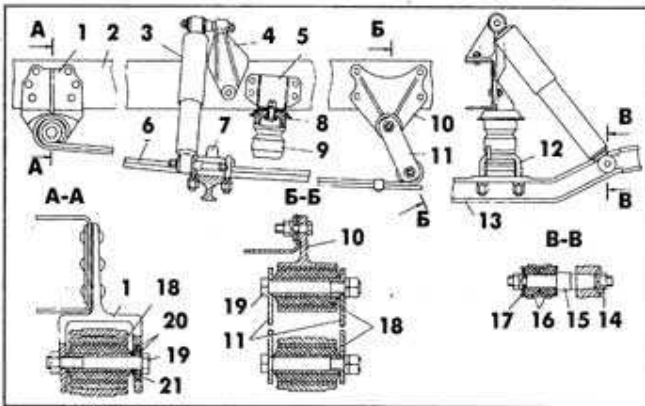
Передняя подвеска автомобилей типа 4x2: 1, 4, 5 и 10 – кронштейны; 2 – лонжерон рамы; 3 – амортизатор; 6 – рессора; 7 – накладка; 8 – чашка; 9 – резиновая рессора сжатия; 11 – серьга; 12 – стремянка; 13 – балка; 14 – гайка; 15 – палец; 16 – резиновые втулки; 17, 20 и 21 – шайбы; 18 – резинометаллические шарниры; 19 – болт.
